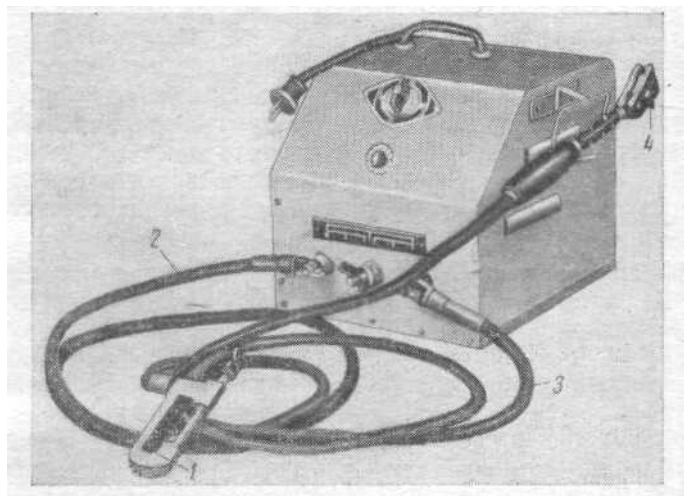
Аппарат НИИАТа для сварки-пайки тонколистового материала
